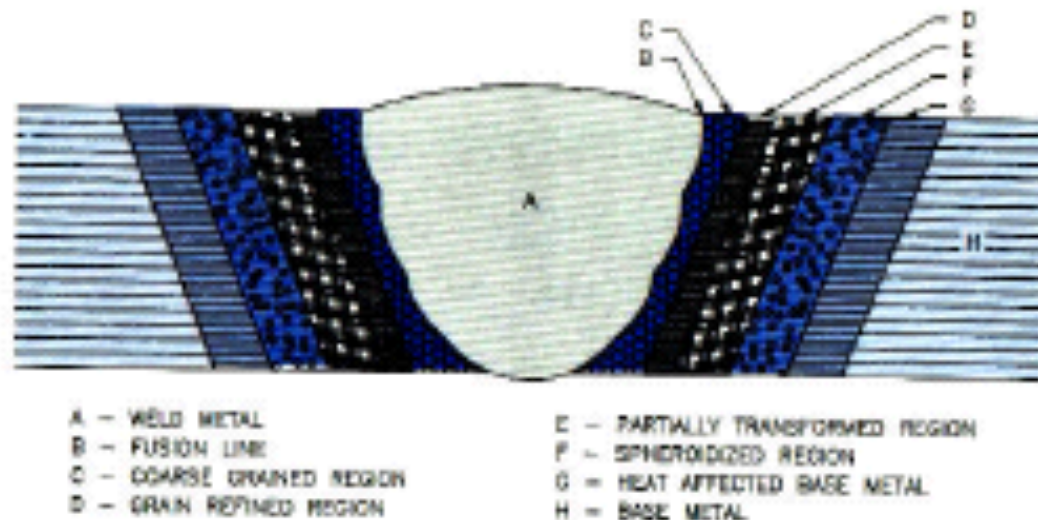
Esquema de la Microestructura de una Soldadura de un acero micro aleado. Welding Journal Mayo
